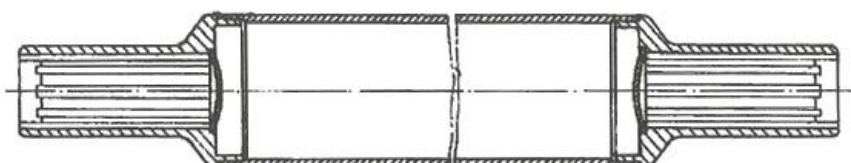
Dělený spojovací hřídel Cardanova mechanismu
